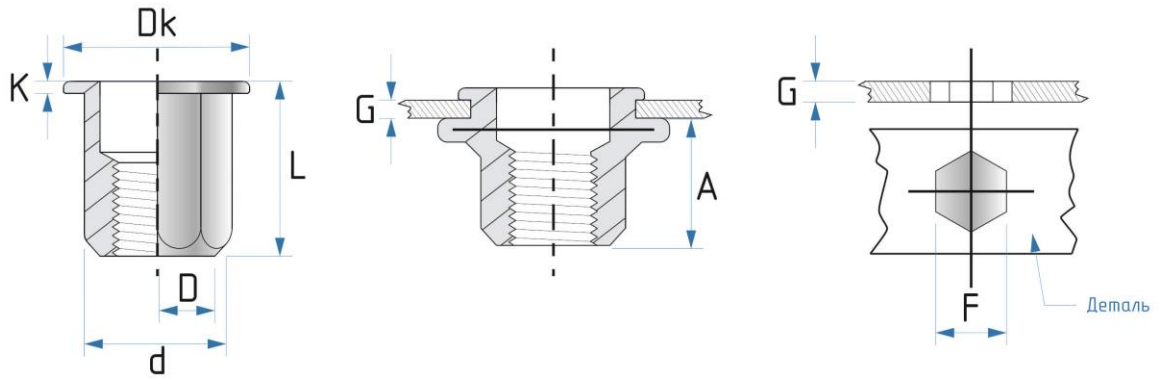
Заклёпка резьбовая шестигранная, стандартный борт,
